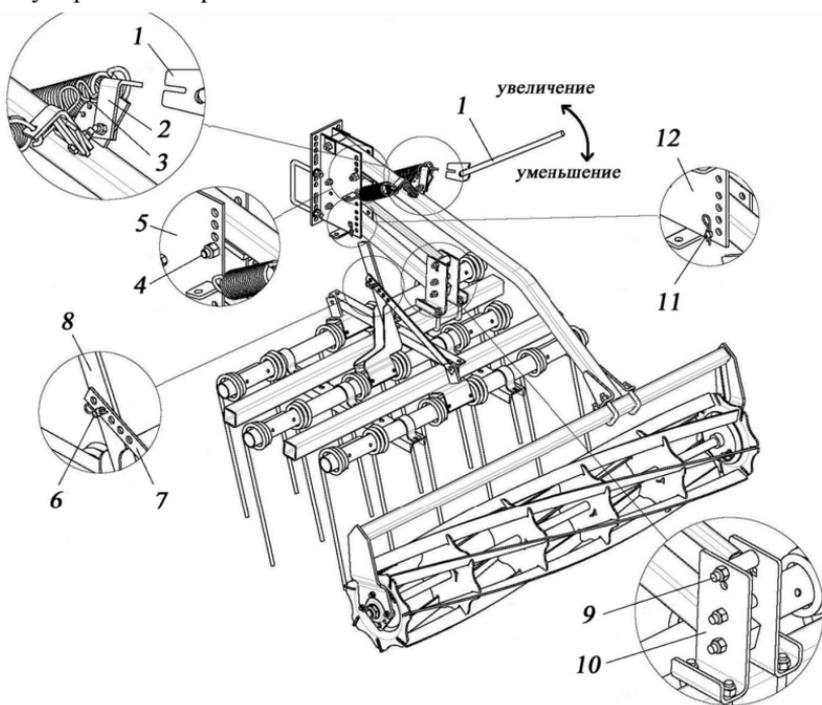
Регулировки ребристого катка и зубовой борны
